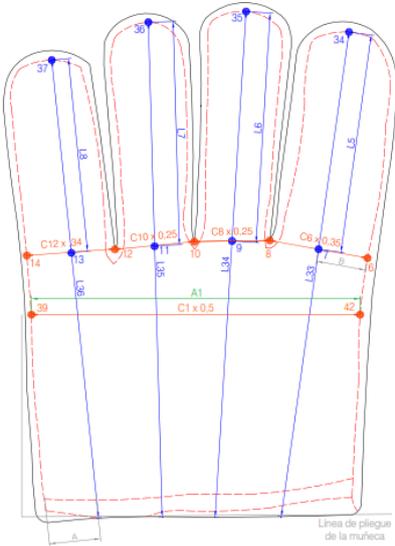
15: Dimensiones utilizadas para el diseño del dorso del guante con pulgar incrustado
